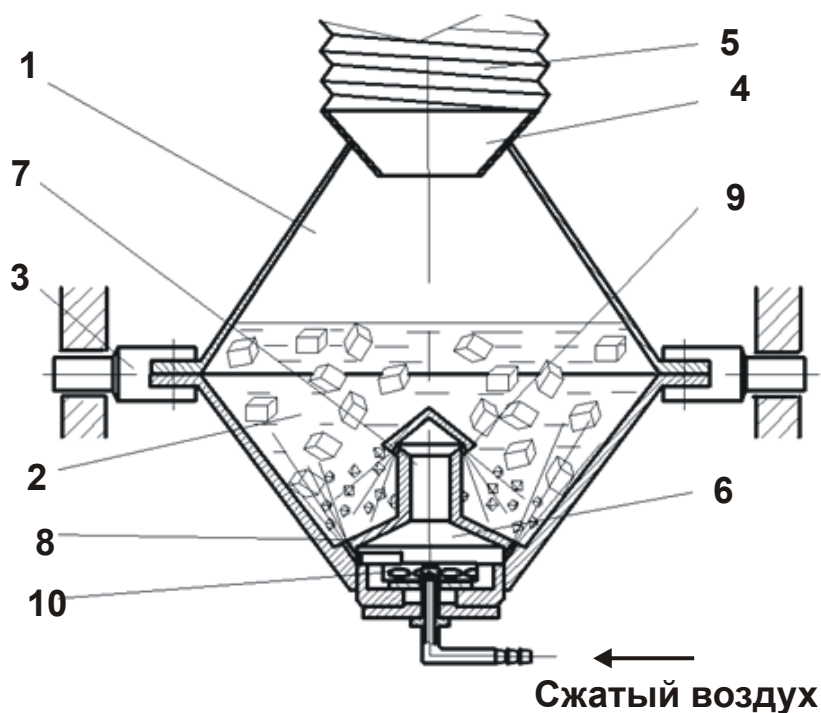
Схема установки для обработки мелких деталей затопленными струями по А. с. № 38676 [14]
